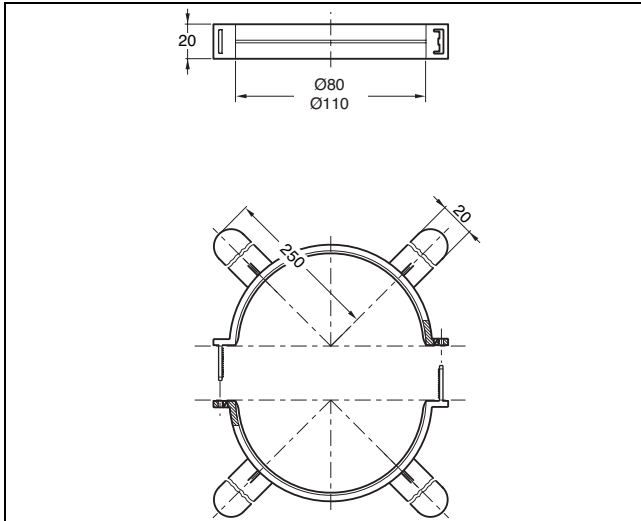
Abstandshalter für Abgasleitung im Schacht (Maße in mm)
